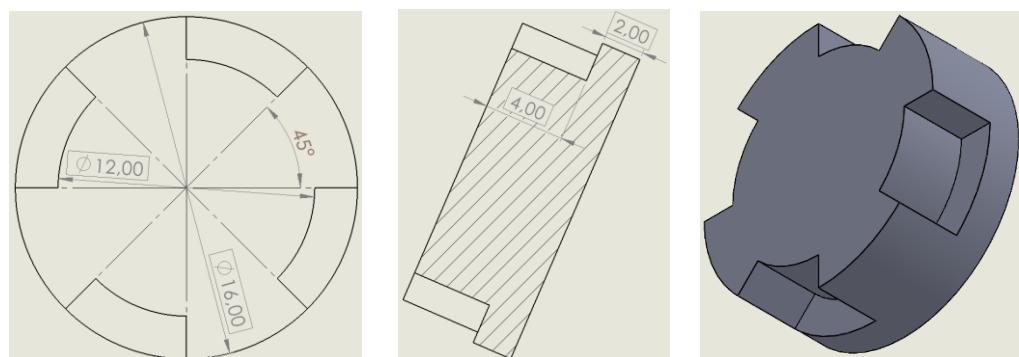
Geometría y dimensiones de la pieza 3, hecha en SolidWorks.
